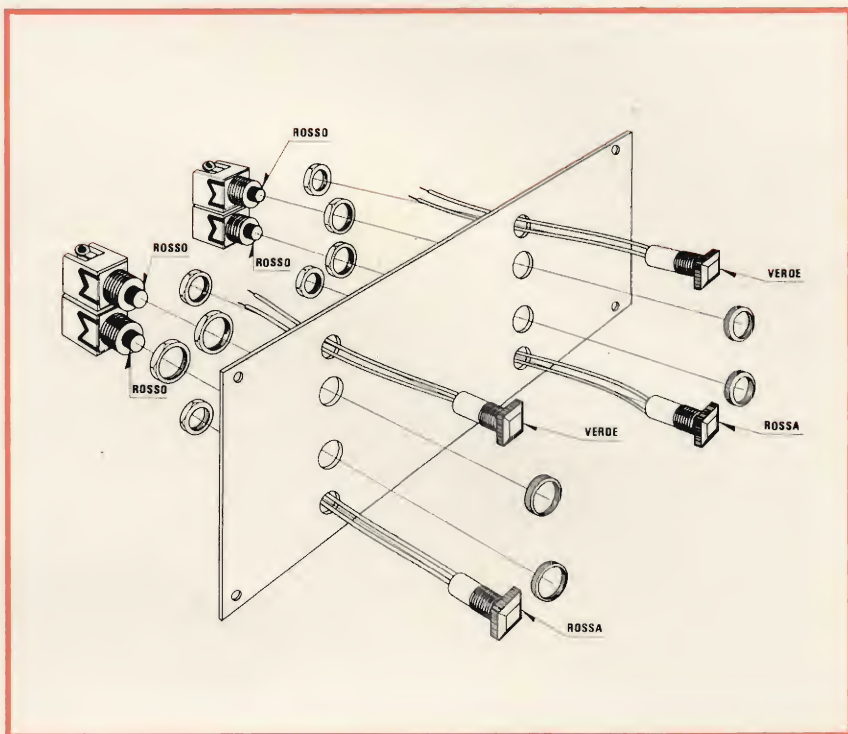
Esploso di montaggio del pannello frontale della scatola di montaggio AMTRON UK 830.
